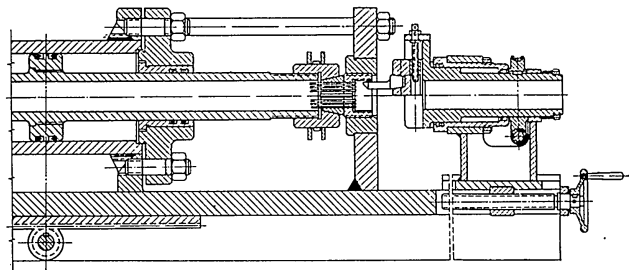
Формирование арматурных пучков ББРФ на специальном прессе (пысадка головок на концах проволоки)
